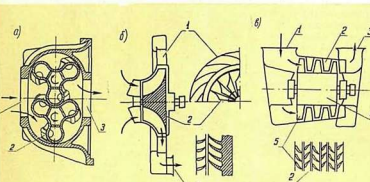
Виды нагнетателей: а — роторно-шестеренчатый: 1 — вход воздуха; 2 — ротор; 3 — выход воздуха; б — центробежный: 1 — лопаточный диффузор; 2 — крыльчатка; 3 — воздухохоборник («улитка»); в — осевой: 1 — вход воздуха; 2 — лопатки нагнетателя; 3 — выход воздуха; 4 — ротор нагнетателя; 5 — лопатки ротора.
